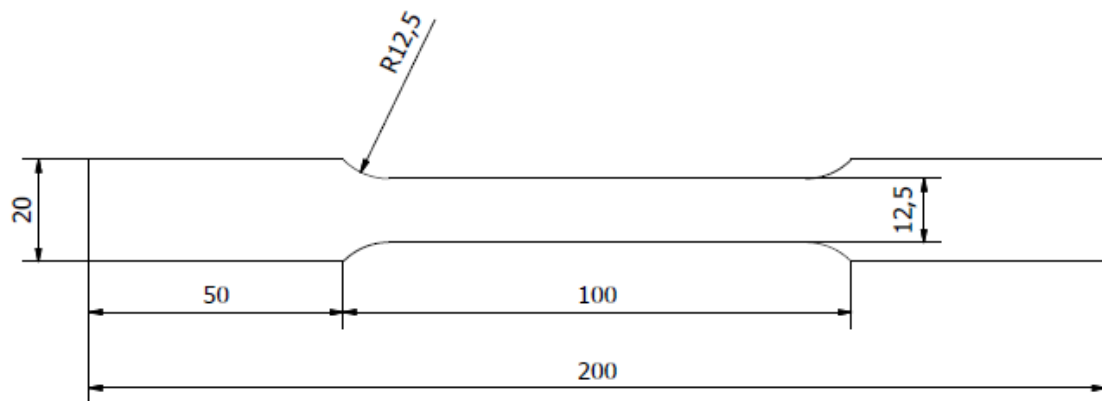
Esquema Posición Junta Soldada
